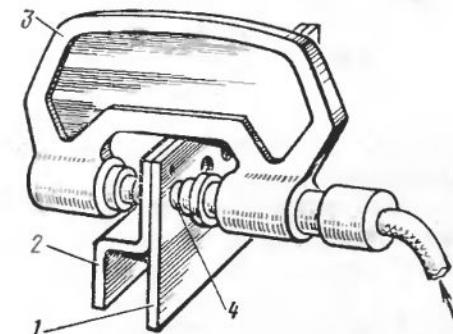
Клепка прессованием с помощью переносной скобы
